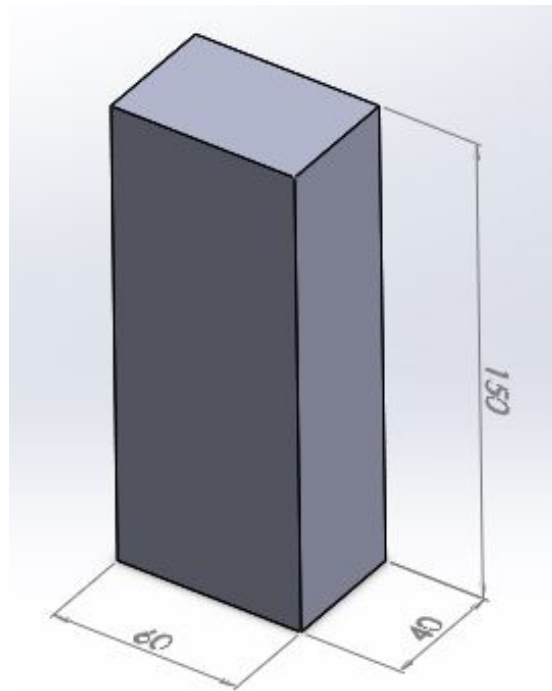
Fabricación. Bloque de aluminio 7075-T6.
